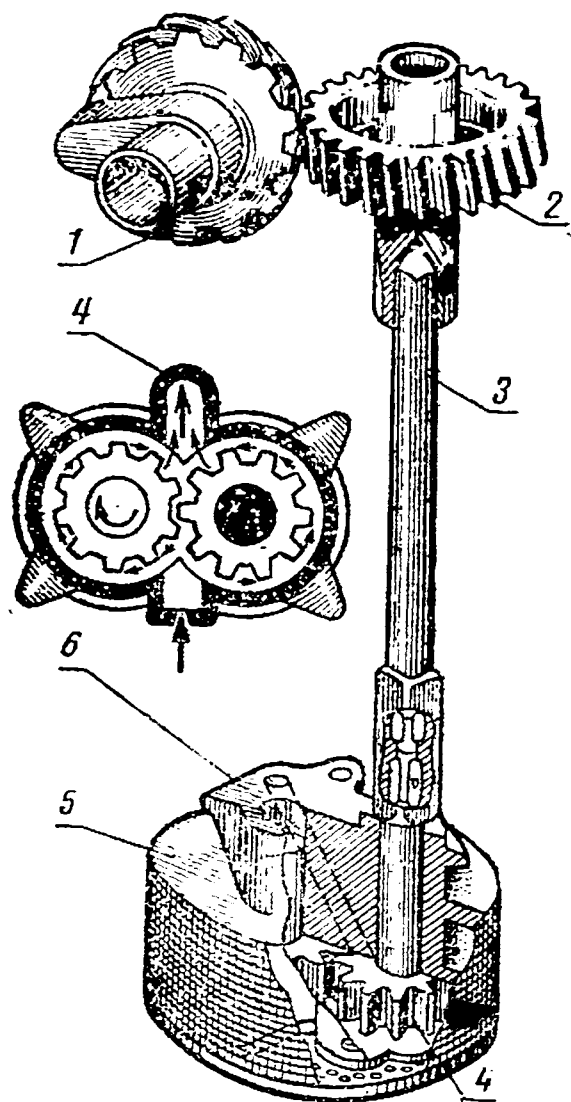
Шестеренчатый масляный насос двигателя К-750 и «Урал»:
